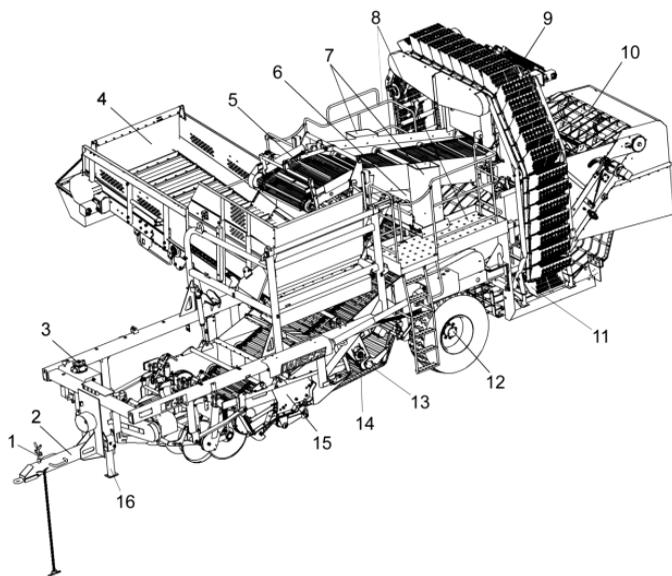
Комбайн картофелеуборочный полуприцепной ПКК-2-02 (с бункером и переборочным столом):
